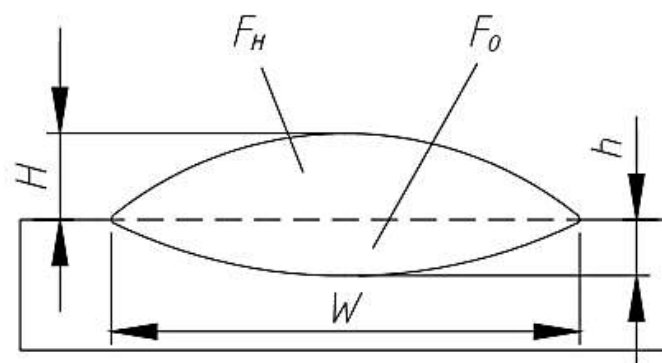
Геометрические параметры наплавленного валика: F_O – площадь подплавленного основного металла; F_H – площадь наплавленного металла; H – высота наплавленного слоя; h – глубина подплавления; W – ширина наплавленного слоя
